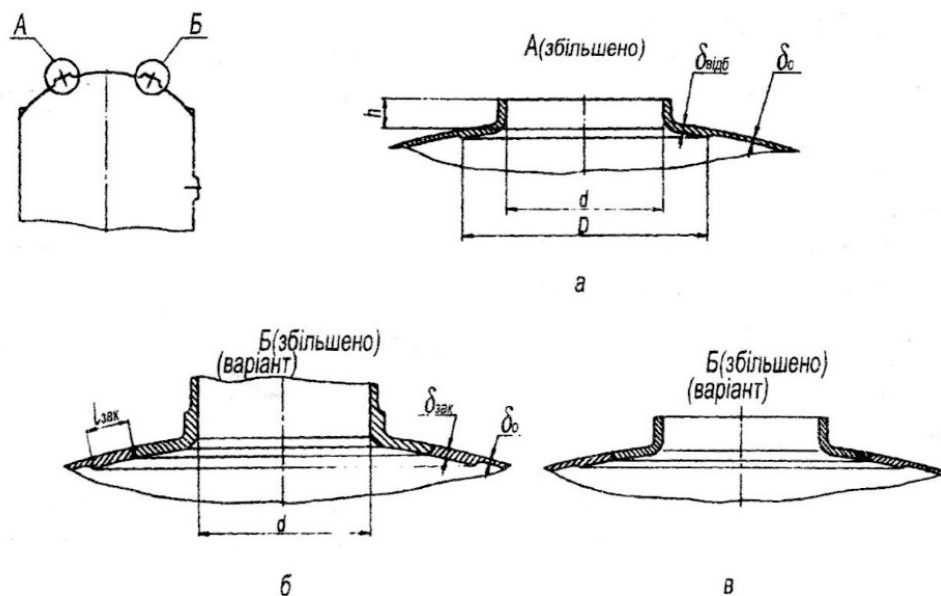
Конструктивні способи установки арматури на корпусі бака:
